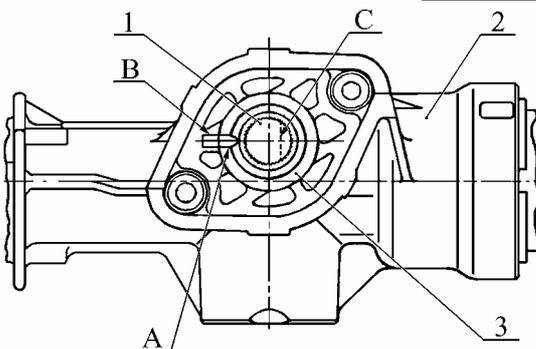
Проверка положения шестерни рулевого механизма ВАЗ-1118:
